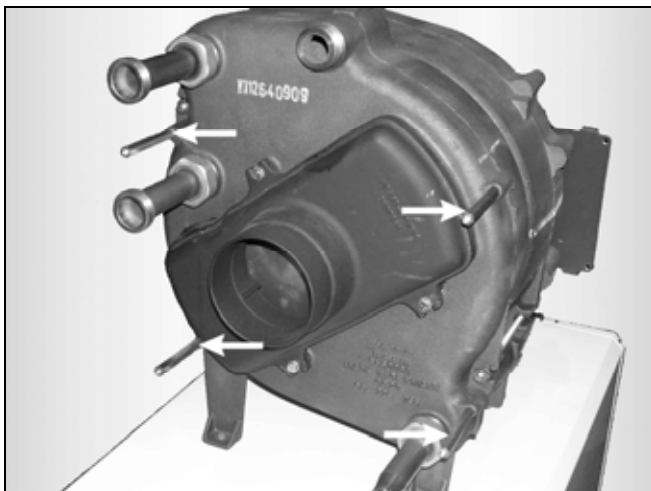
Die Distanzstücke für die hintere Blechverkleidung montieren.
